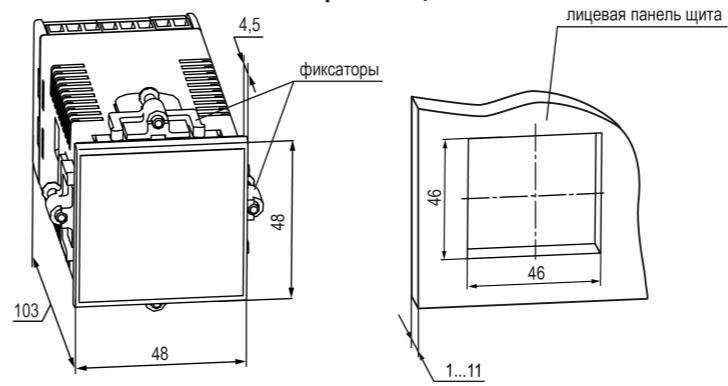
Габаритные размеры корпуса Щ5 и монтажного отверстия в щите
